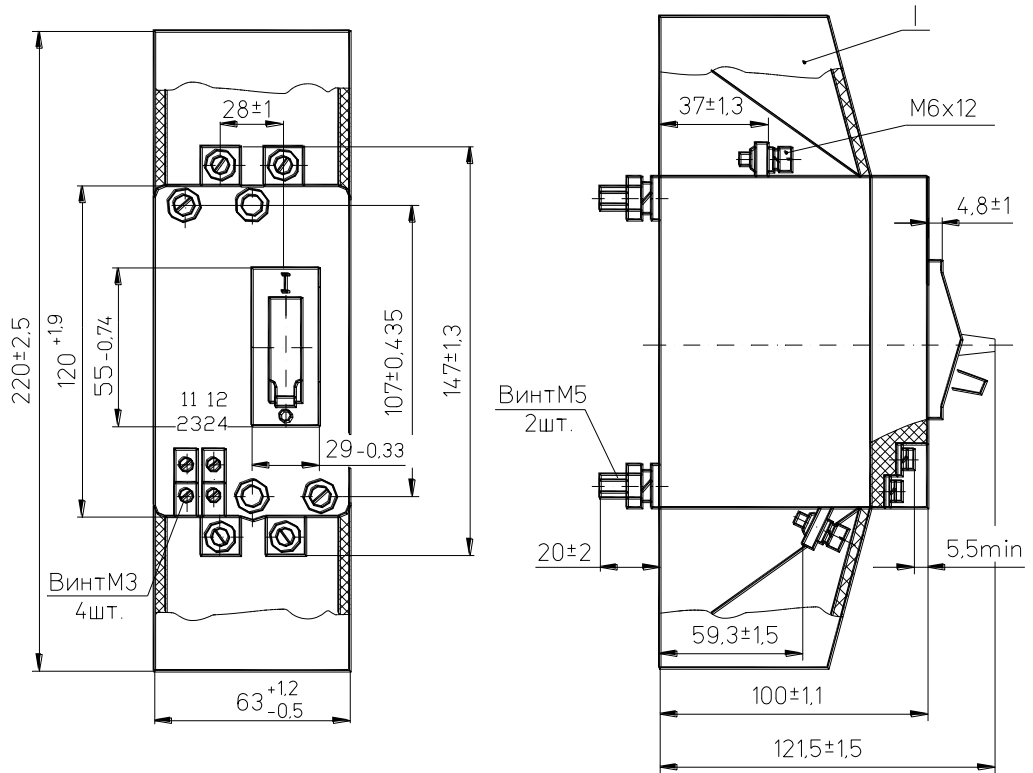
Сверление отверстий под винты крепления однополюсного выключателя:
